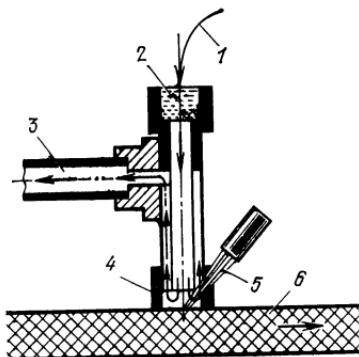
Разрез вакуумной головки для очистки пластинок:
